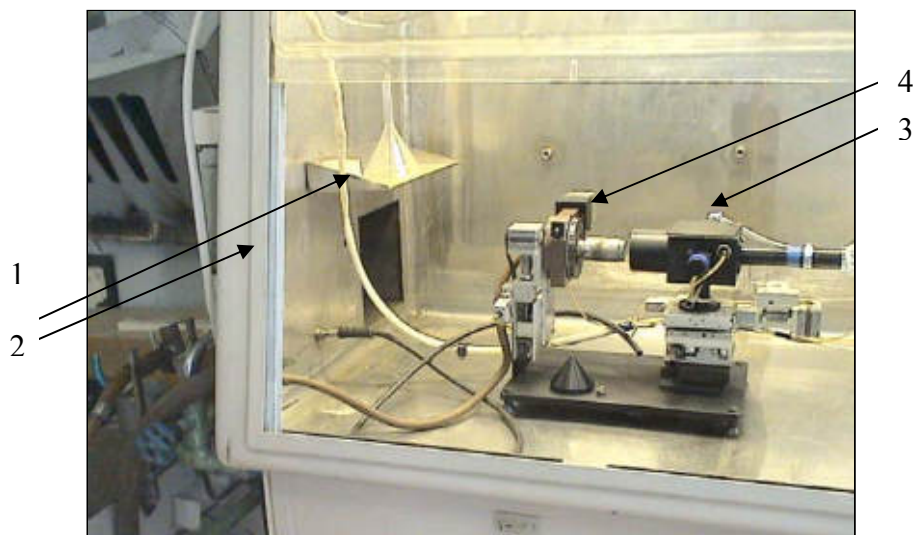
Общий вид установки лазерной сварки, размещенной в боксе:
